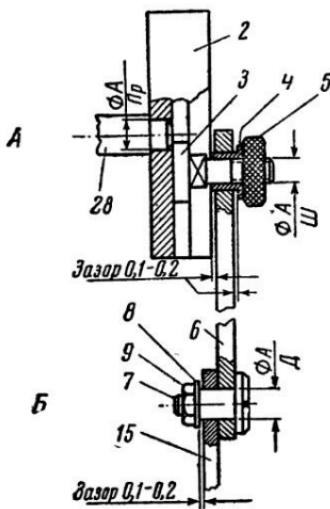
Модель механизма подачи стола поперечно-строгального станка (схема соединения деталей): А — узел привода механизма (2 — диск регулирования величины подачи, 3 — установочный палец, 4 — упорная втулка, 5 — гайка с накаткой, 28 — вал привода); Б — узел соединения тяги с коромыслом (6 — тяга, 7 — ось, 8 — шайба, 9 — гайка, 15 — коромысло).
